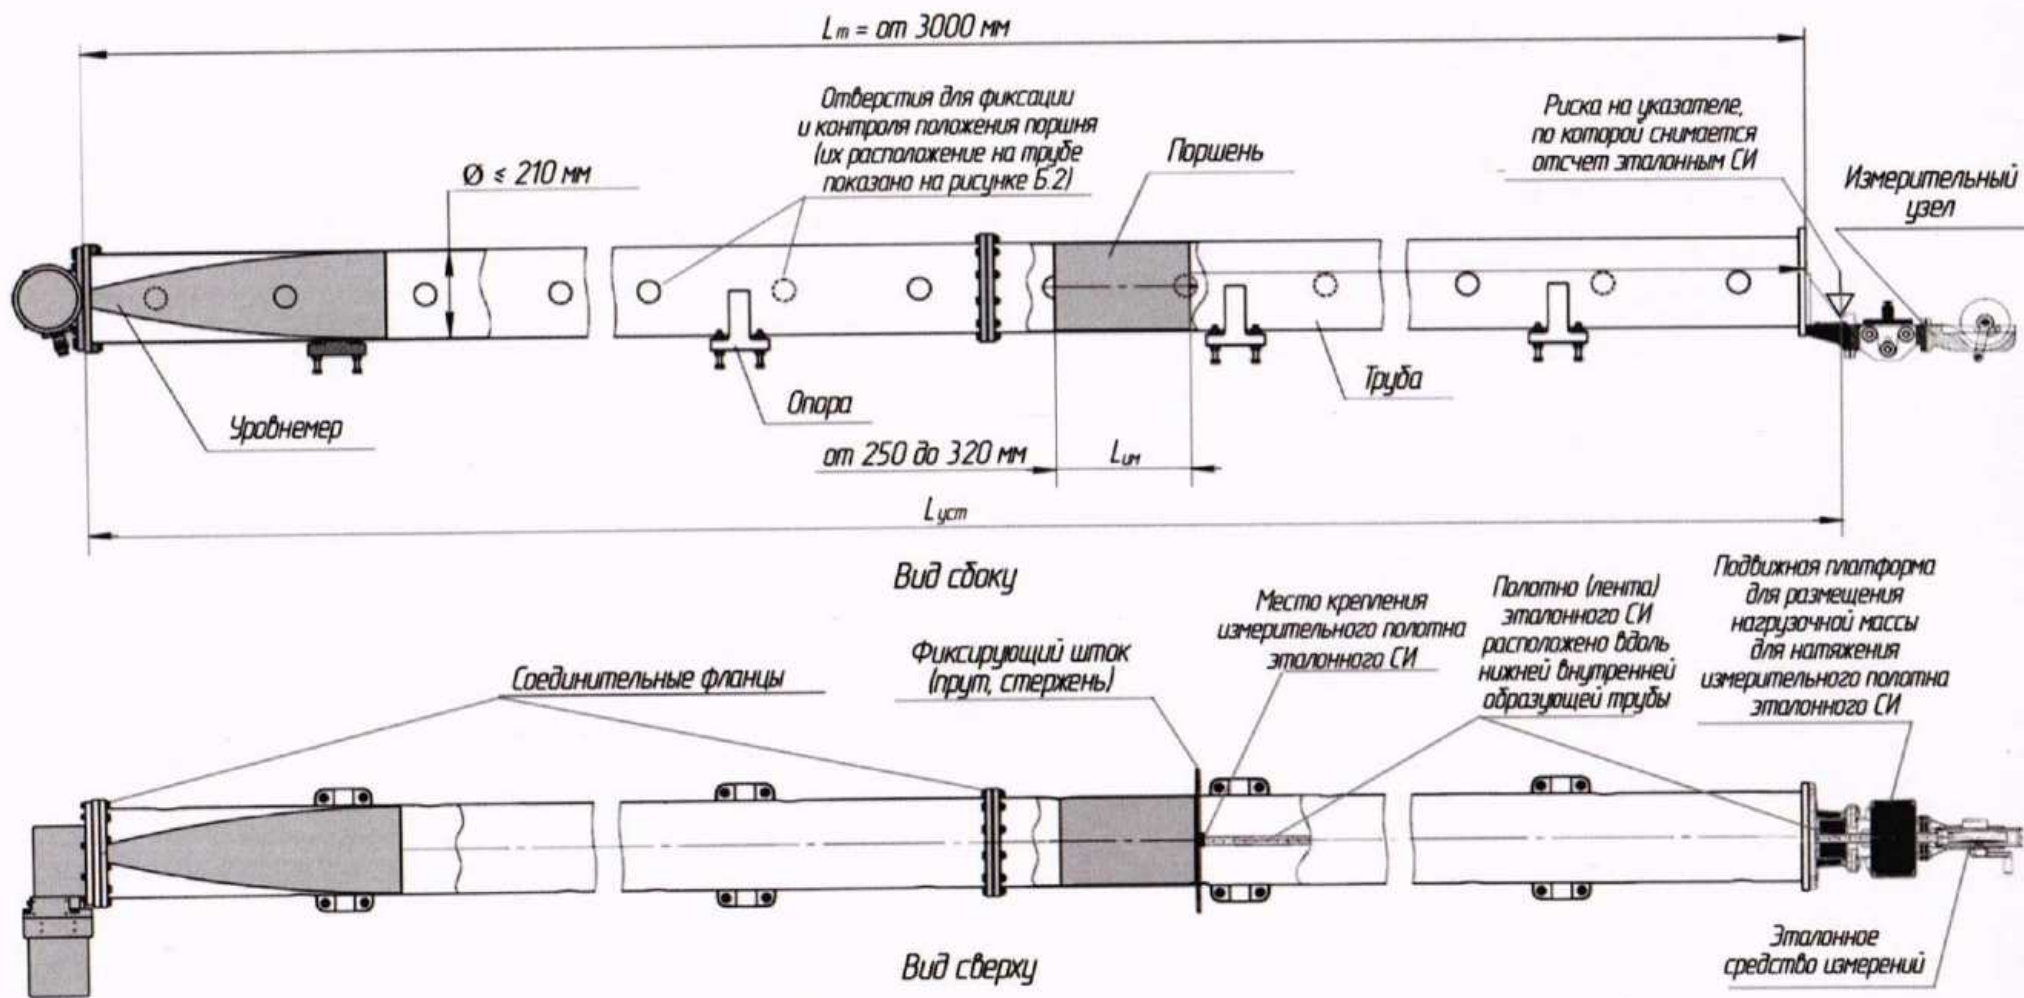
Конструктивная схема имитатора поверхности продукта (общий вид с размерами и обозначениями)
